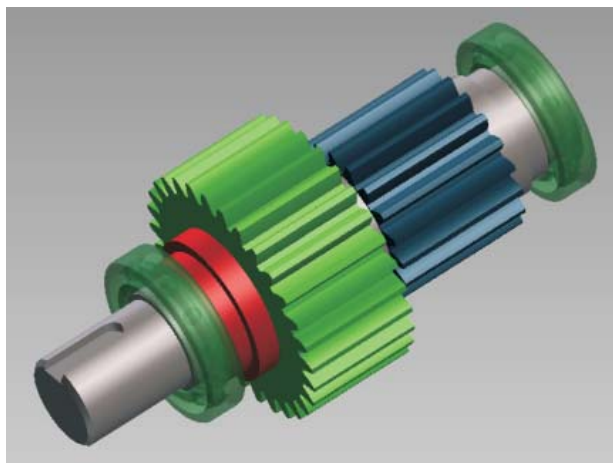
3D-модель узла промежуточного вала редуктора в сборе
